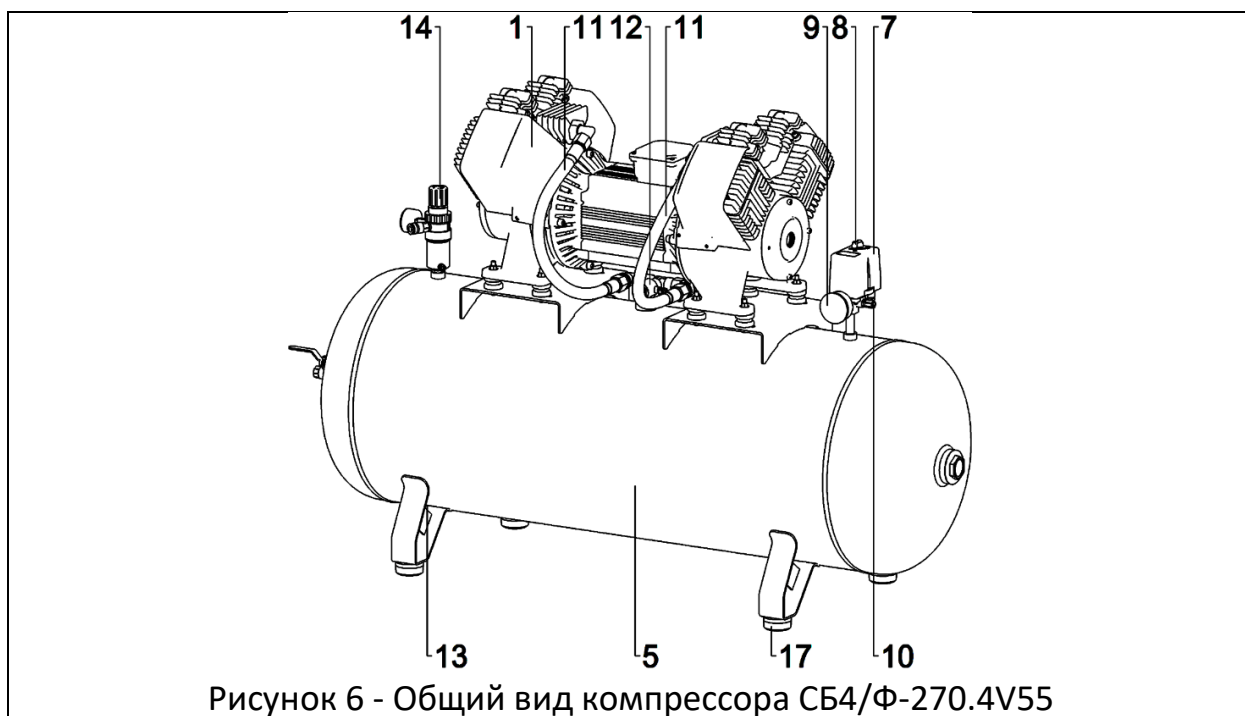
Общий вид компрессора СБ4/Ф-270.4V55
